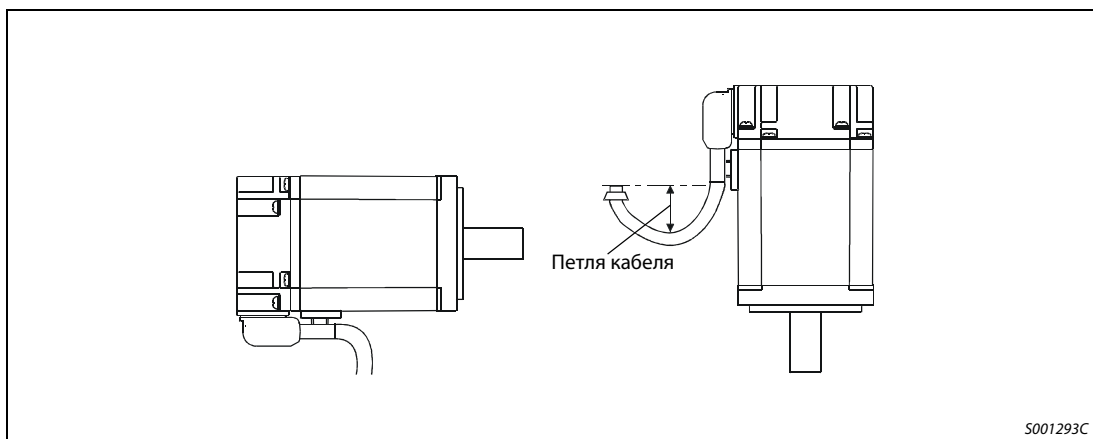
Горизонтальный или вертикальный монтаж серводвигателя с петлей кабеля
